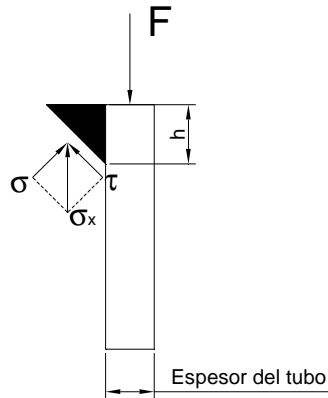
Análisis de cuerpo libre para la soldadura
